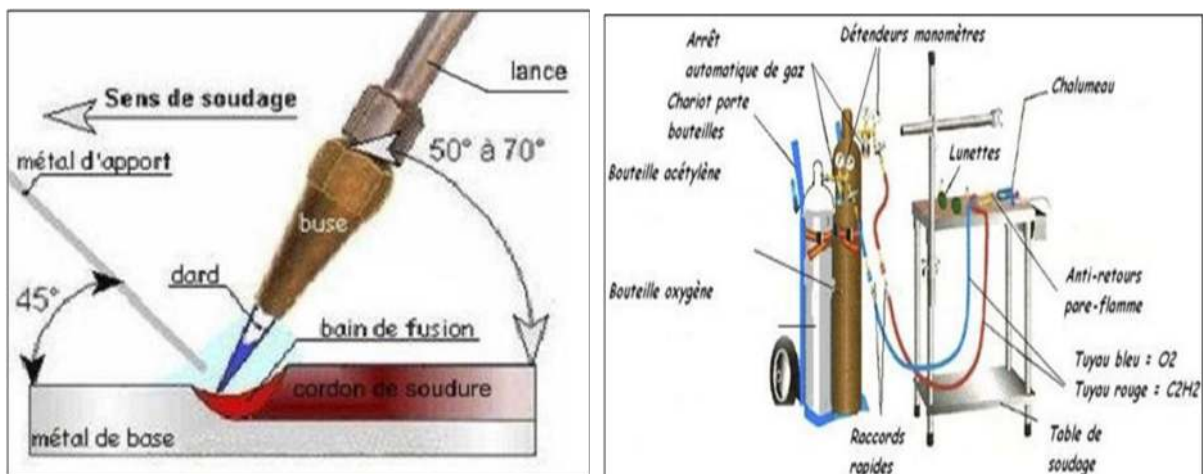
7: Matériel propre au soudage oxyacétylénique
